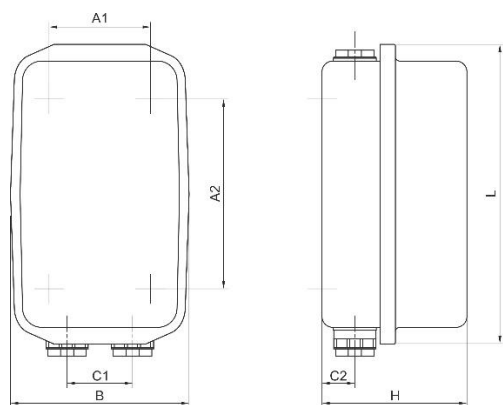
Пускатель ПМ12 100-180А в защитном корпусе.
